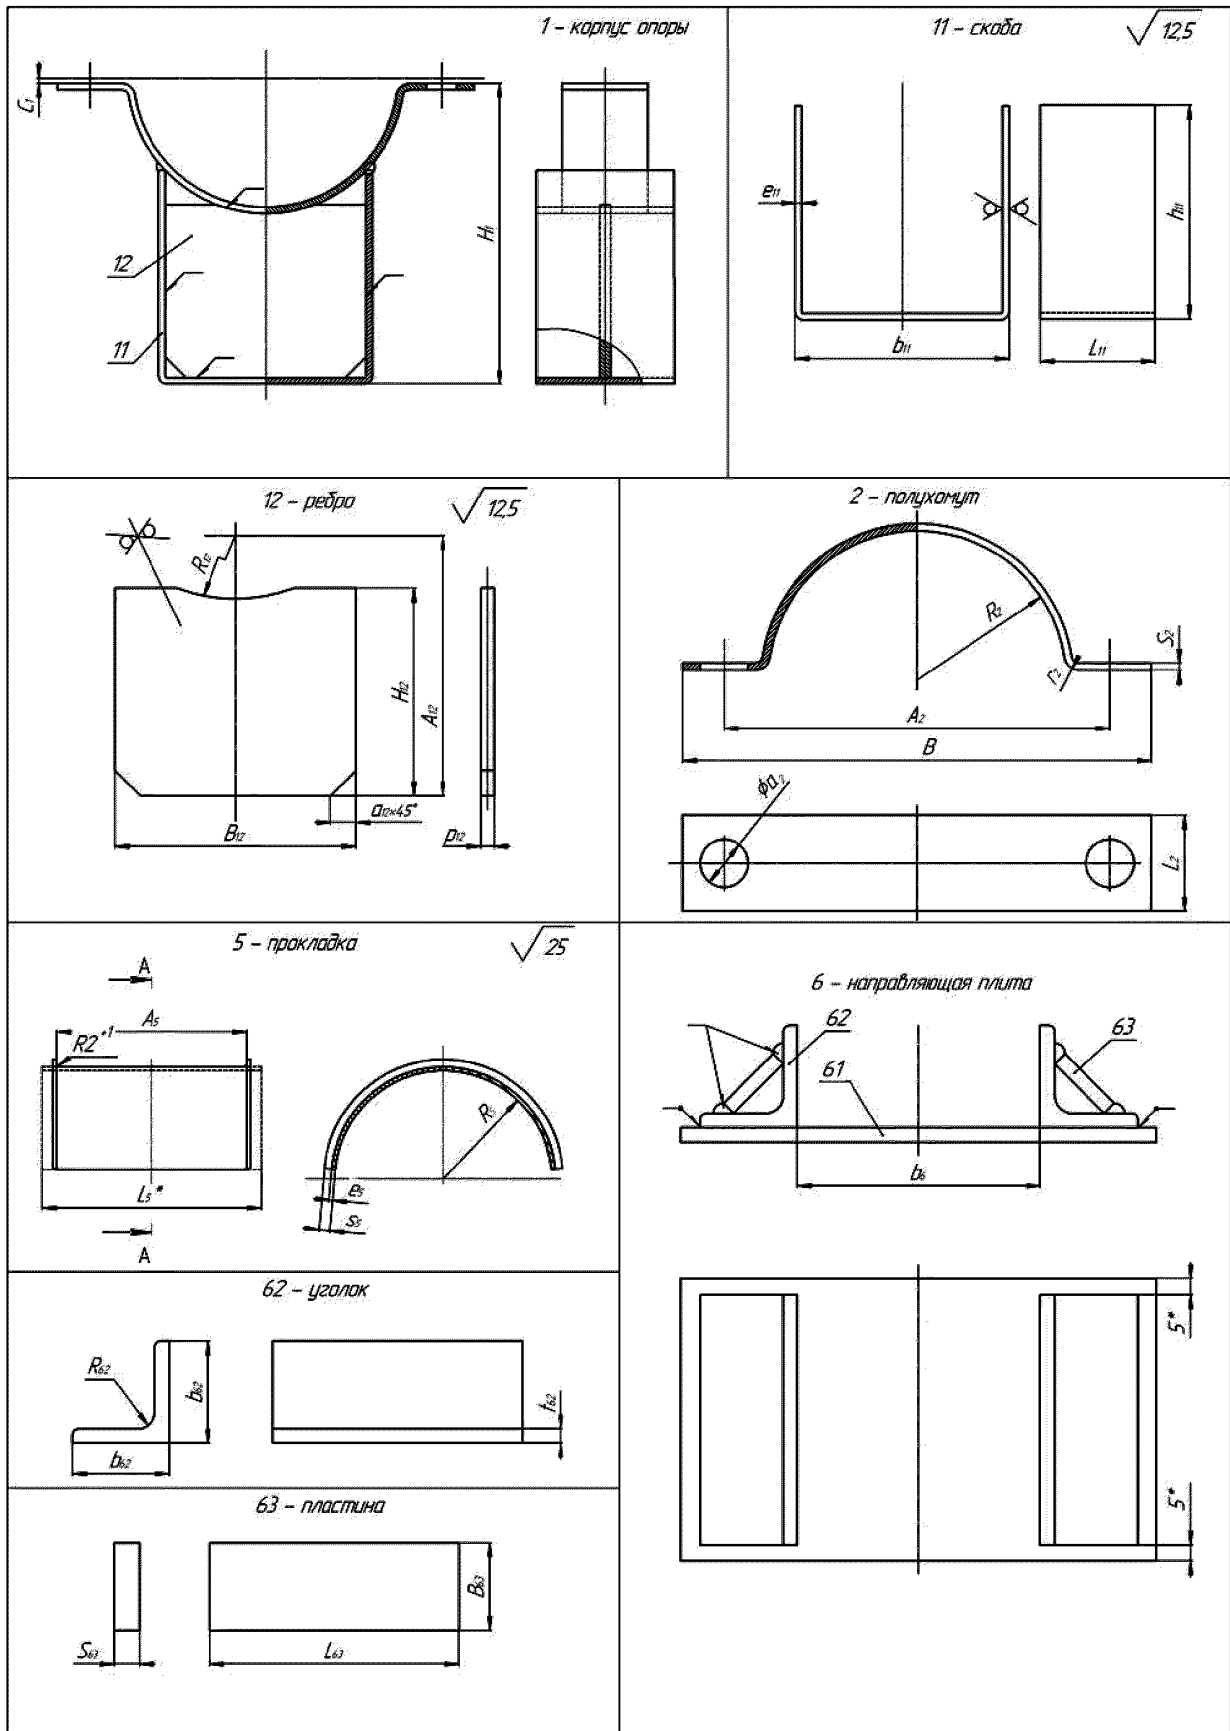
Детали изделий 01-XXXX-G-1С-02-В для
